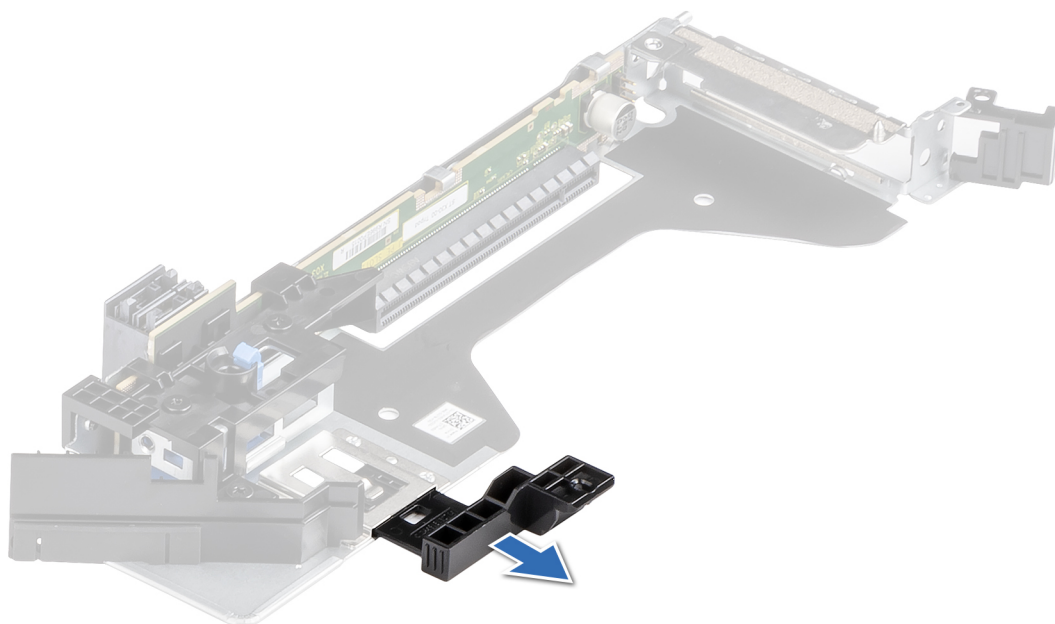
Ouverture du support de carte sur la carte de montage pour carte d'extension
